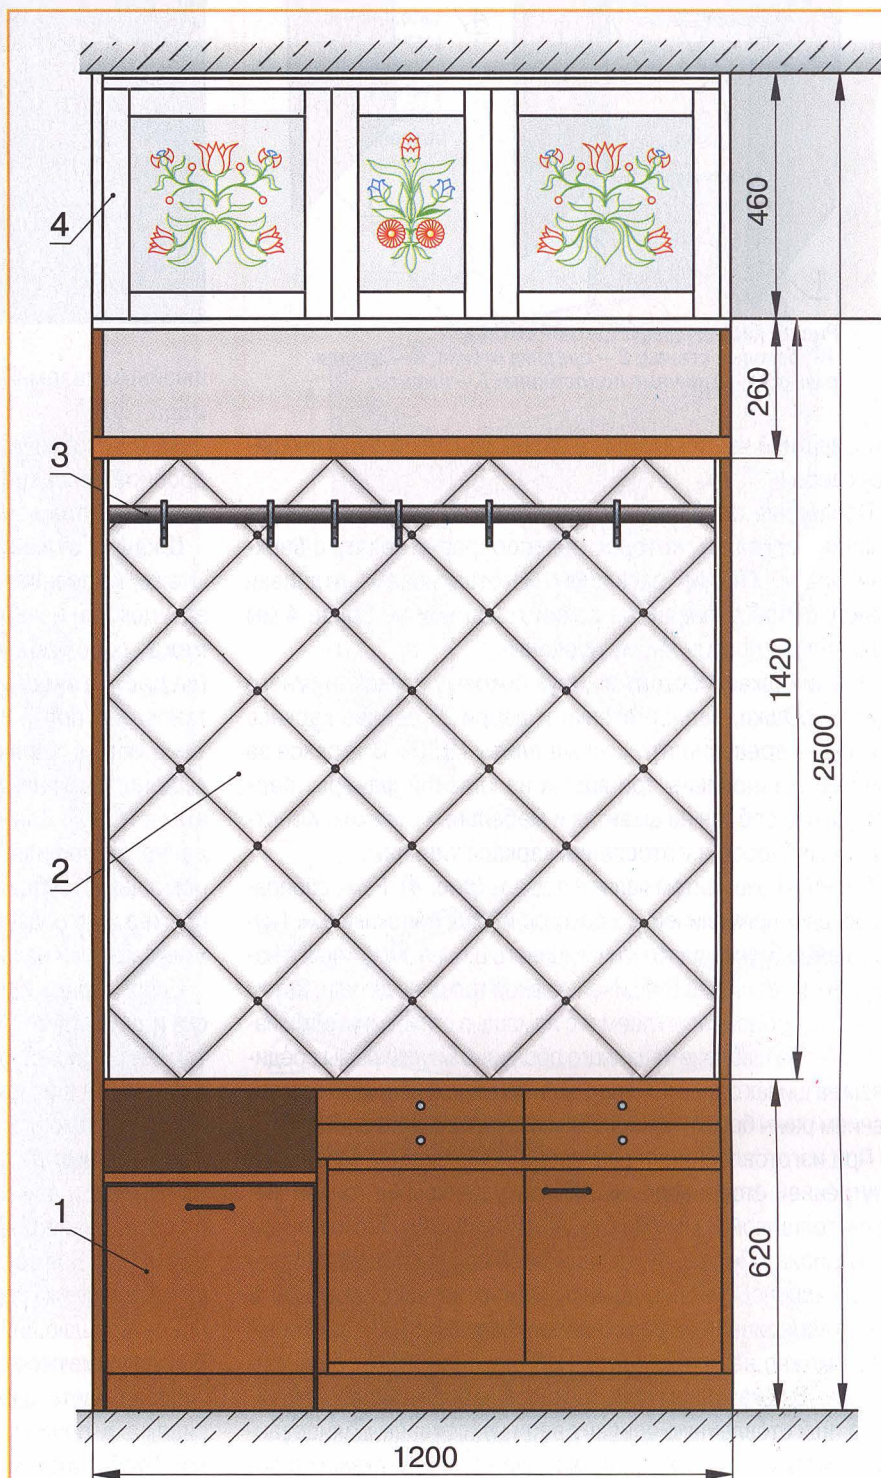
Общий вид шкафа для прихожей: 1 — банкетка; 2 — шкаф; 3 — штанга; 4 — антресоль.
